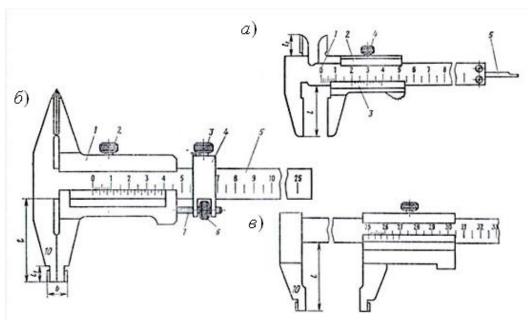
Общий вид и конструкции традиционных нониусных штангенциркулей:
